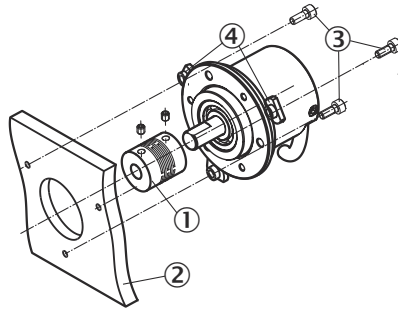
Anbau Klemmflansch mit Servoklammern
